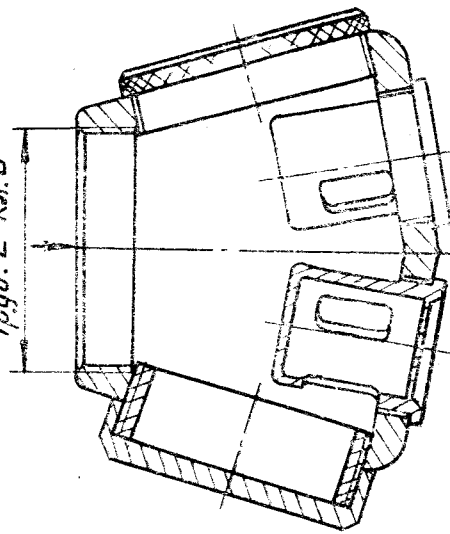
Насадок модульный центробежный РМЦ-1 (черт. 69353-00.000, п/я А-7210)
